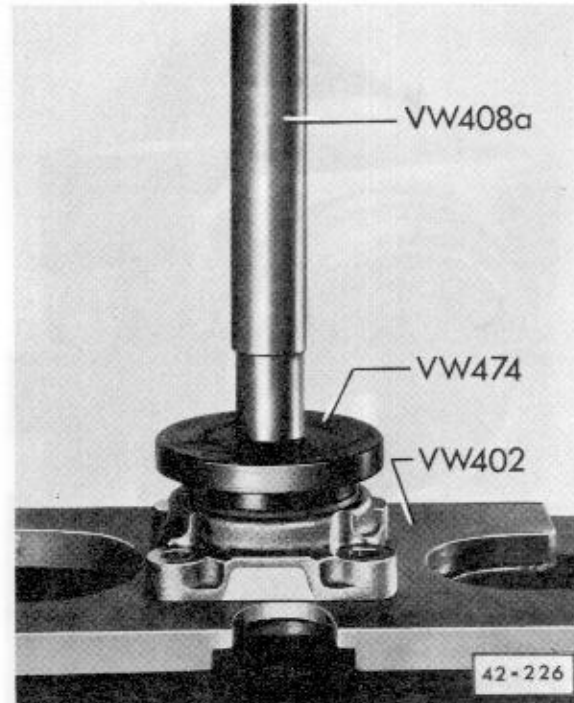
Dichtring in Deckel für Hinterradlager einpressen
